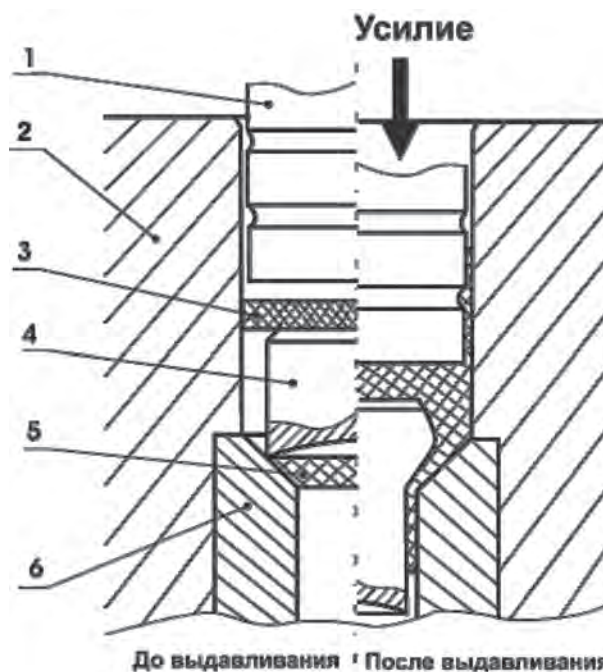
Принципиальная схема процесса выдавливания чугунового прутка: 1 – пуансон; 2 – контейнер штампа; 3 – вкладыш для смазки из электродного графита; 4 – чугуновая заготовка; 5 – конусная матрица; 6 – направляющая втулка
